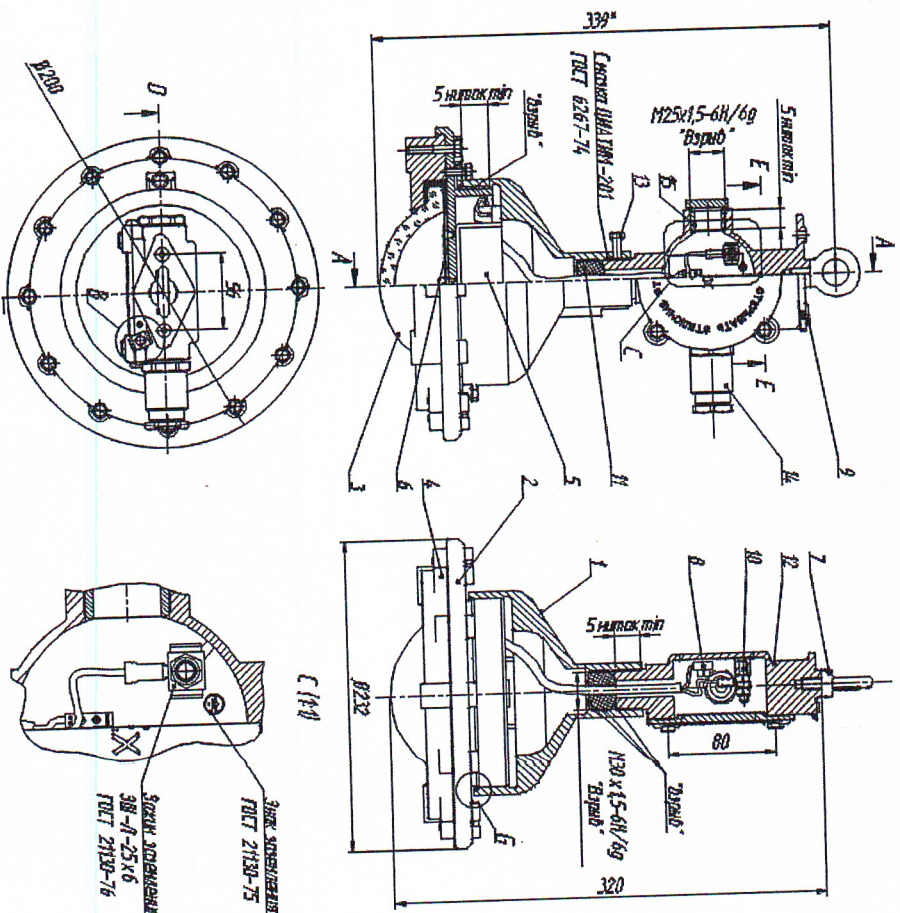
Устройство, габаритные и присоединительные размеры светильника.
